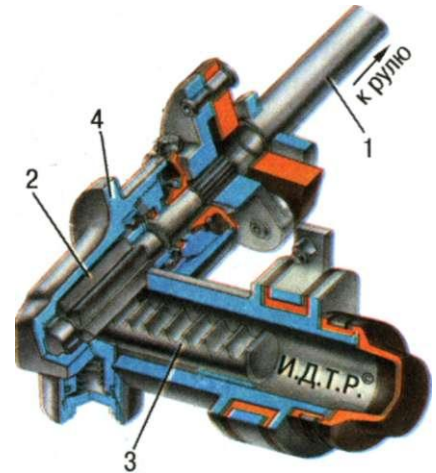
Реечный рулевой механизм: 1 - рулевой вал; 2 - шестерня; 3 - зубчатая рейка; 4 - картер рулевого механизма
